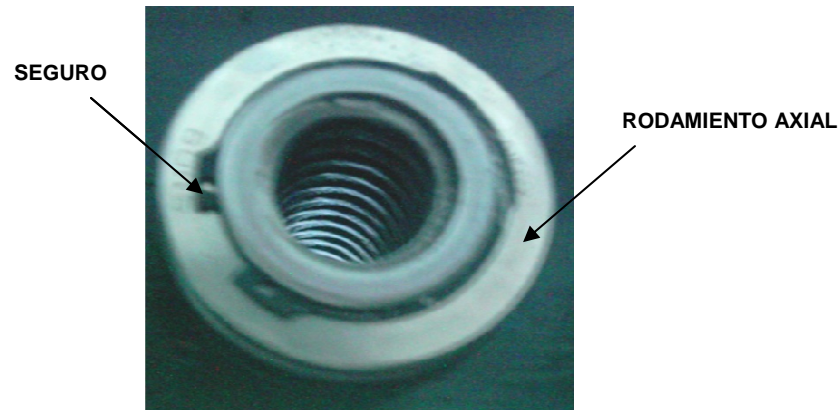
MONTAJE DE RODAMIENTO Y SEGURO
